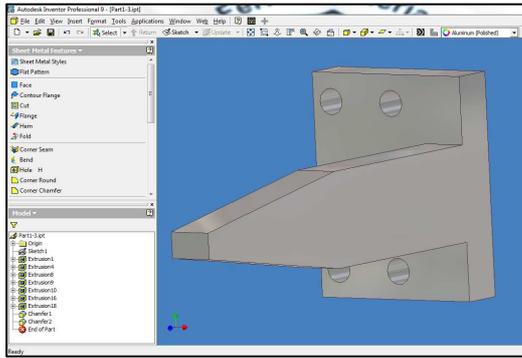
Diseño en Inventor 9.0 de pinza sujetadora
